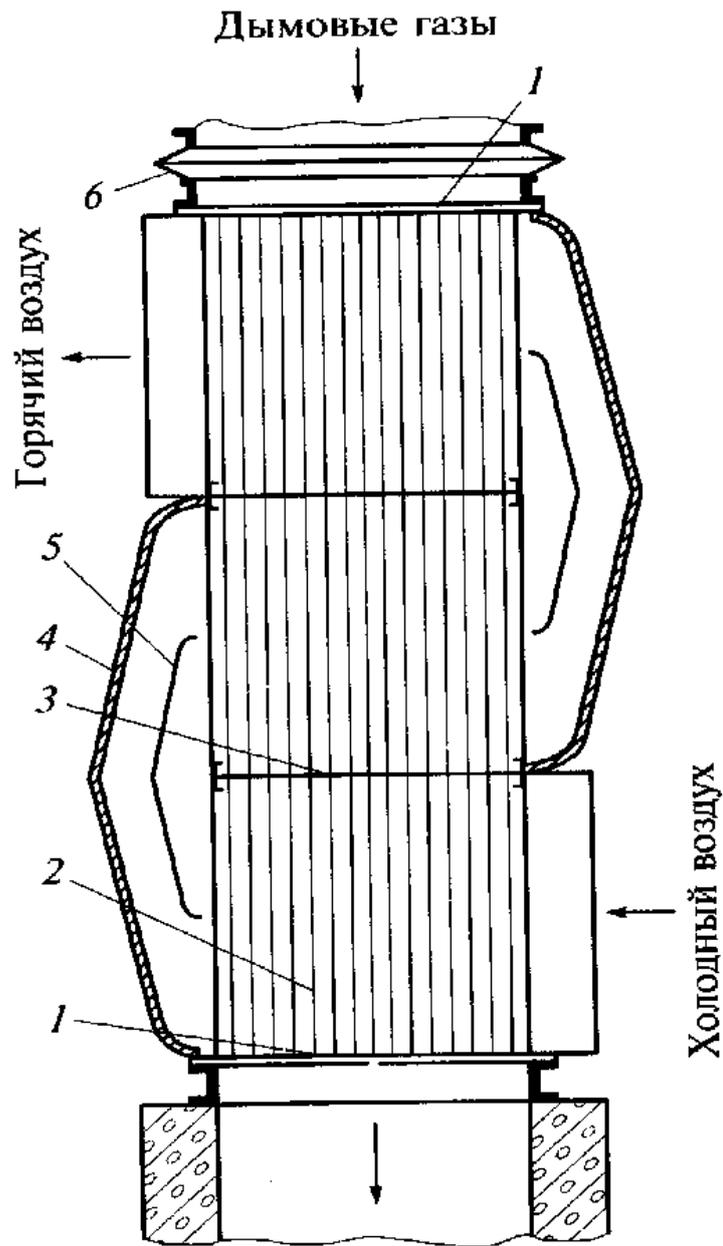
Воздухоподогреватель рекуперативного типа: 7 - трубные доски; 2 - трубы; 3 - перегородка; 4 - кожух; 5 - направляющая лопатка; 6 - линзовый компенсатор
